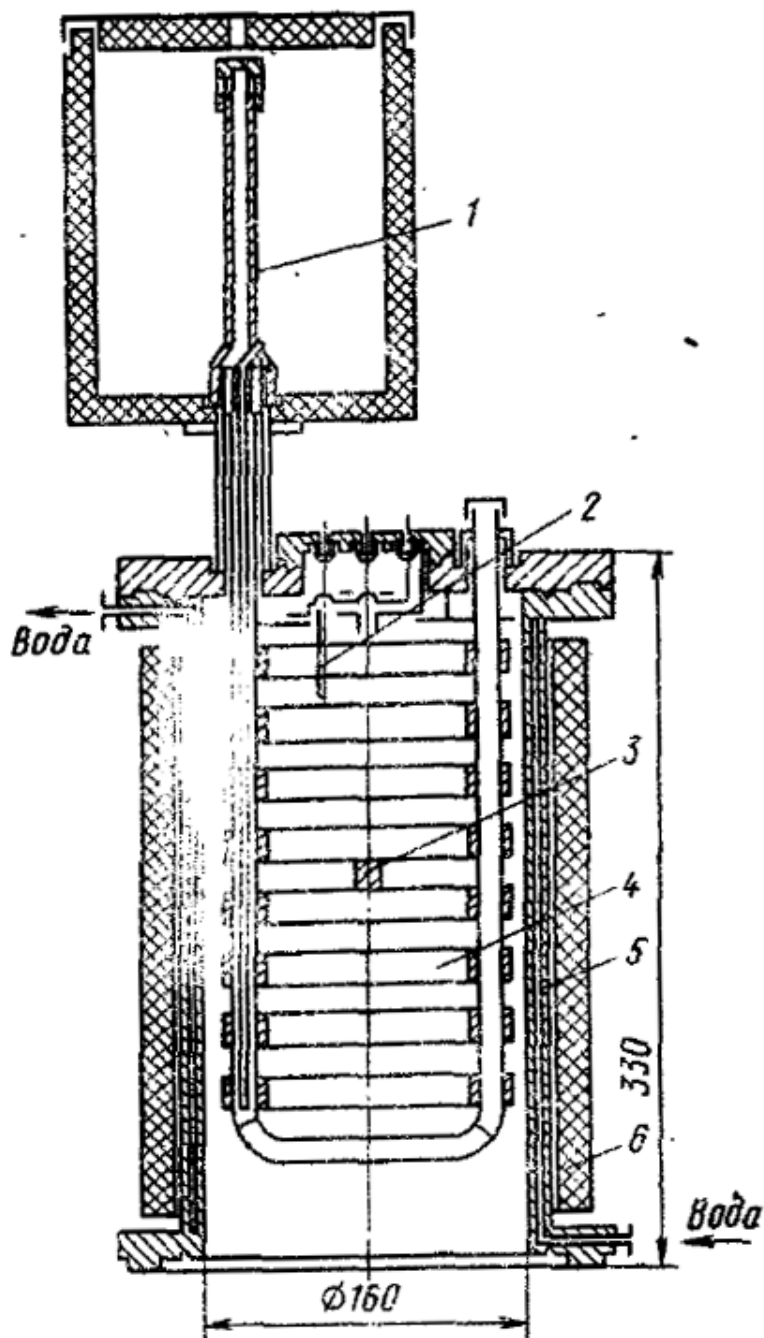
Конструктивная схема насоса СОН-А-1. 1 – азотный питатель; 2 – нить накала; 3 – анод с титановой навеской; 4 – вкладыш с охлаждаемыми кольцами; 5 – корпус с водяной рубашкой; 6 – теплоизоляционный экран [9, с. 361]
